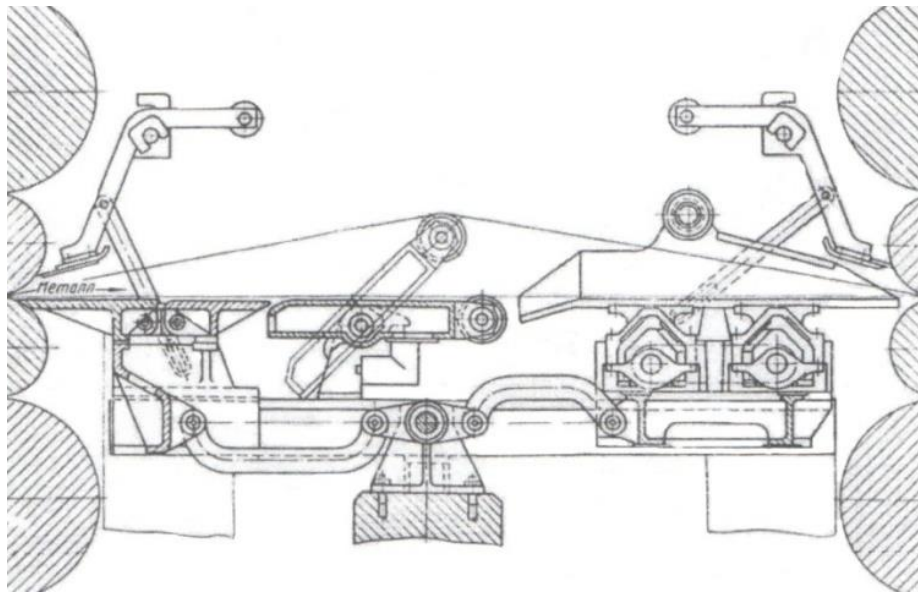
Загальний вид петлетримача між клітьми чистової групи
